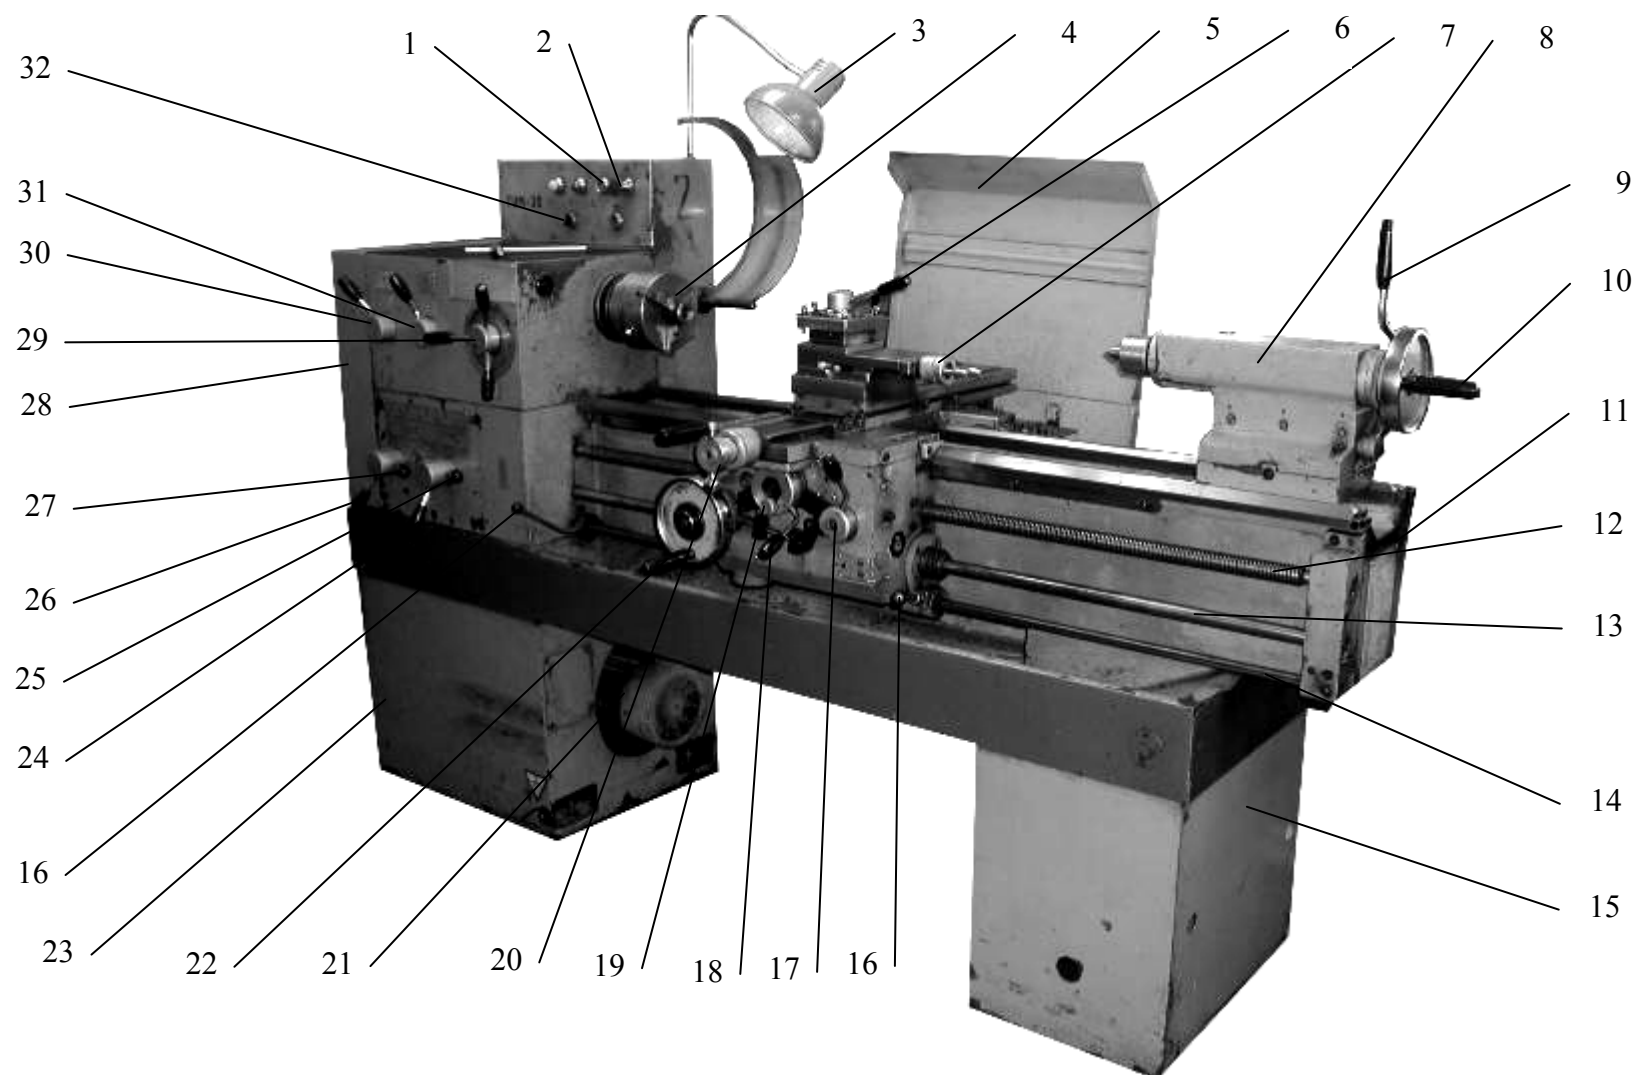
Общий вид токарно-винторезного станка модели TUM-35
